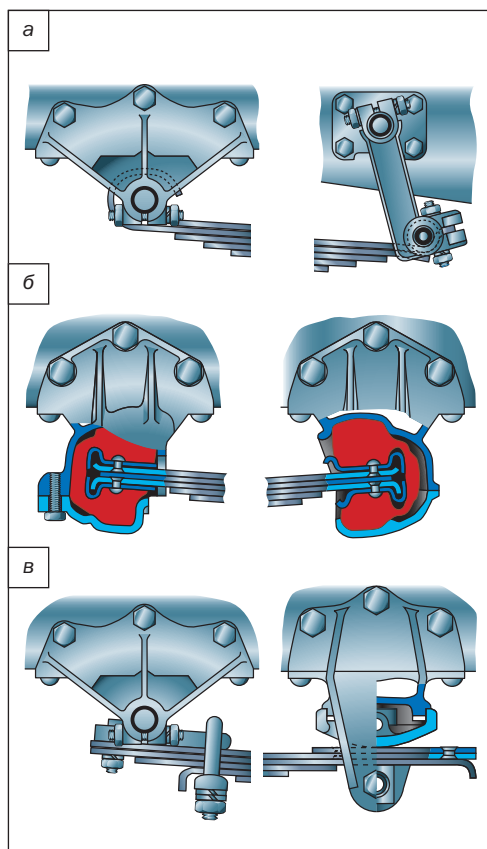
Способы крепления рессор: а — с виштыми ушками; б — на резиновых подушках; в — с накладным ушком и скользящей опорой
